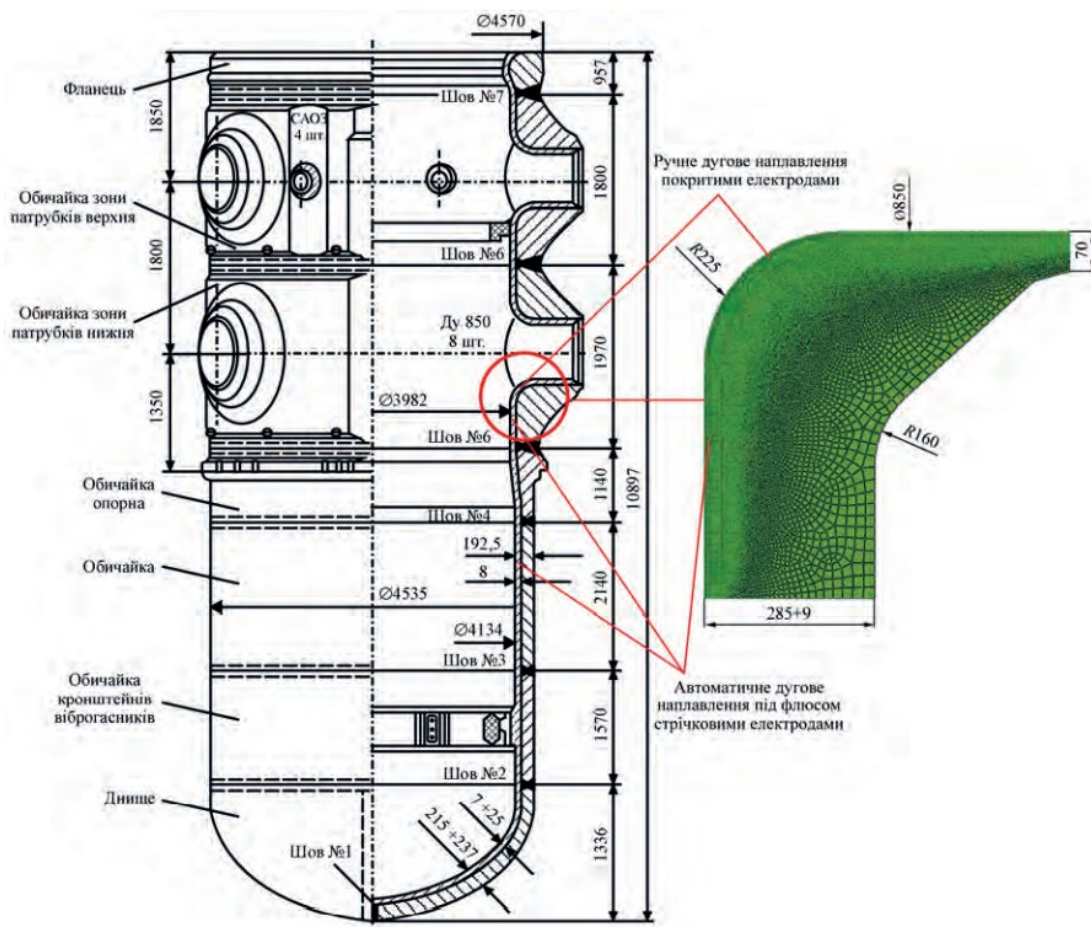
Схема розташування зон ручного та автоматичного наплавлення антикорозійного шару на КР ВВЕР-1000 та скінченноелементна модель патрубкової зони [2].
